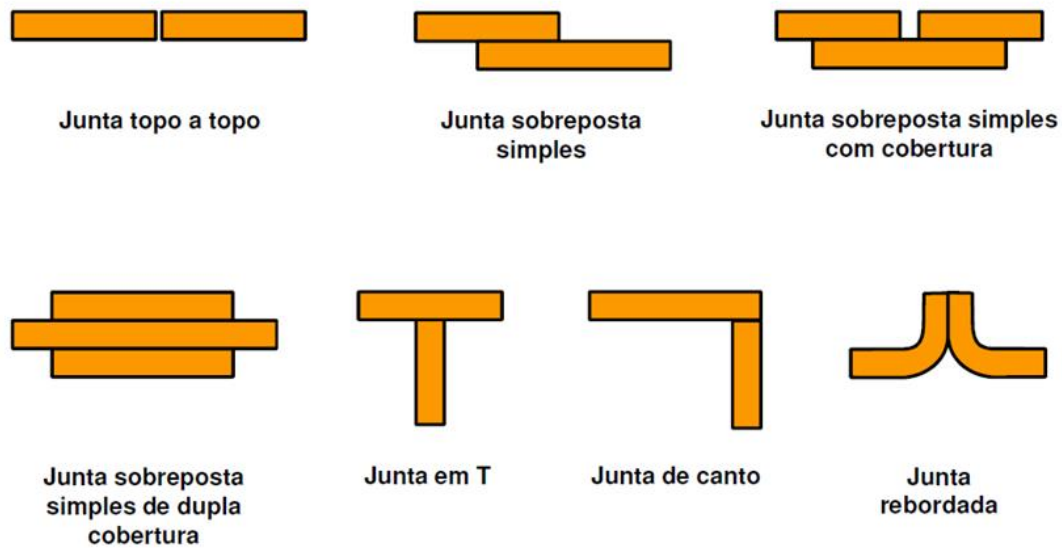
Tipos de juntas de soldadura [16]
